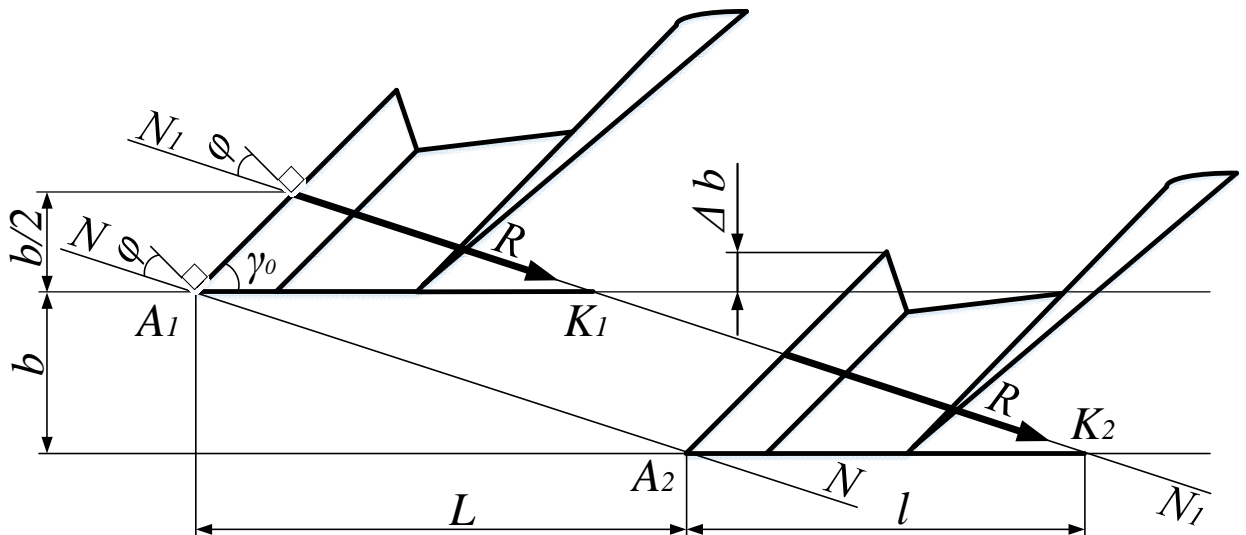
Схема для визначення відстані між корпусами і довжини польової дошки
